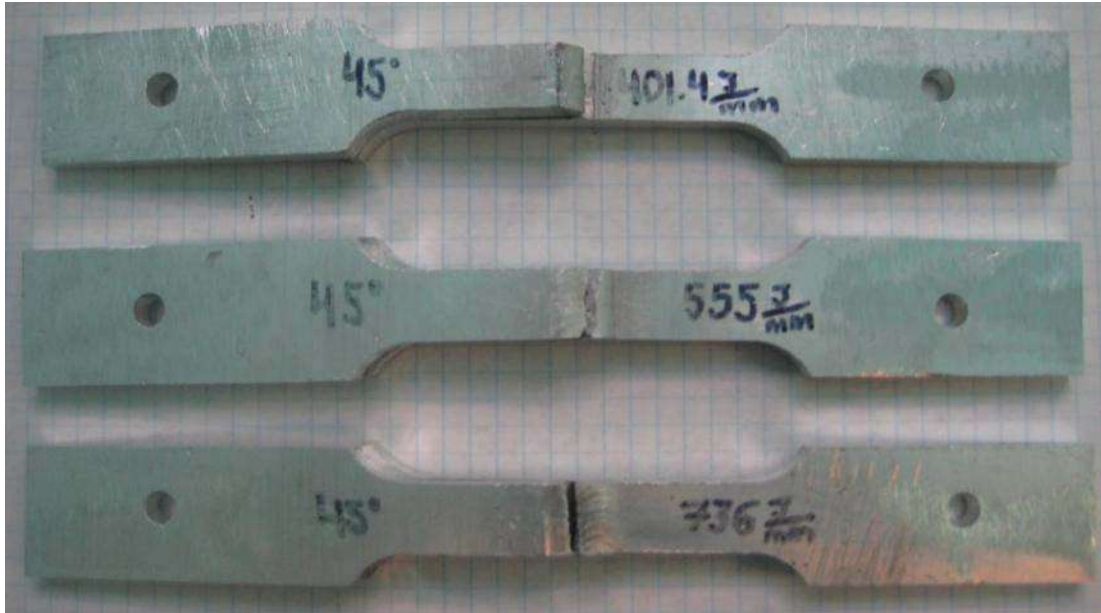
Probetas fracturadas de soldaduras realizadas con un ángulo de 45°
